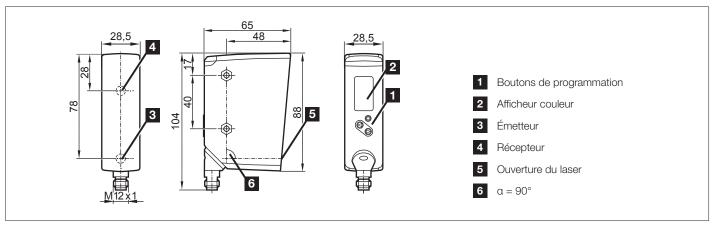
Schéma d'encombrement – Dimensions en [mm]
